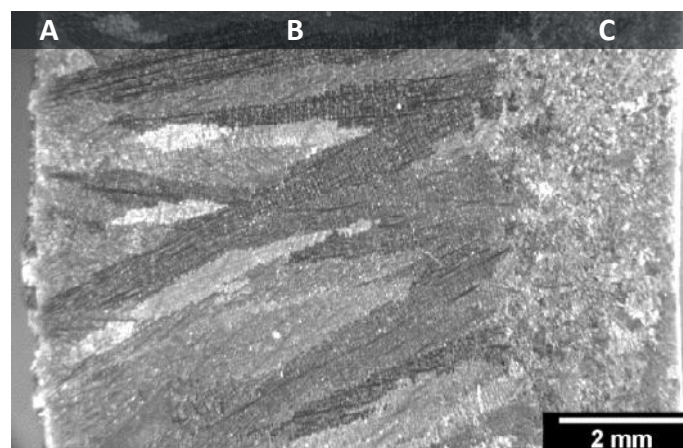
Macroestrutura típica da seção transversal de um tubo fabricado através da técnica de fundição por centrifugação. Em A, zona coquilhada, em B, zona de grãos colunares, em C, zona de grãos equiaxiais [5].
